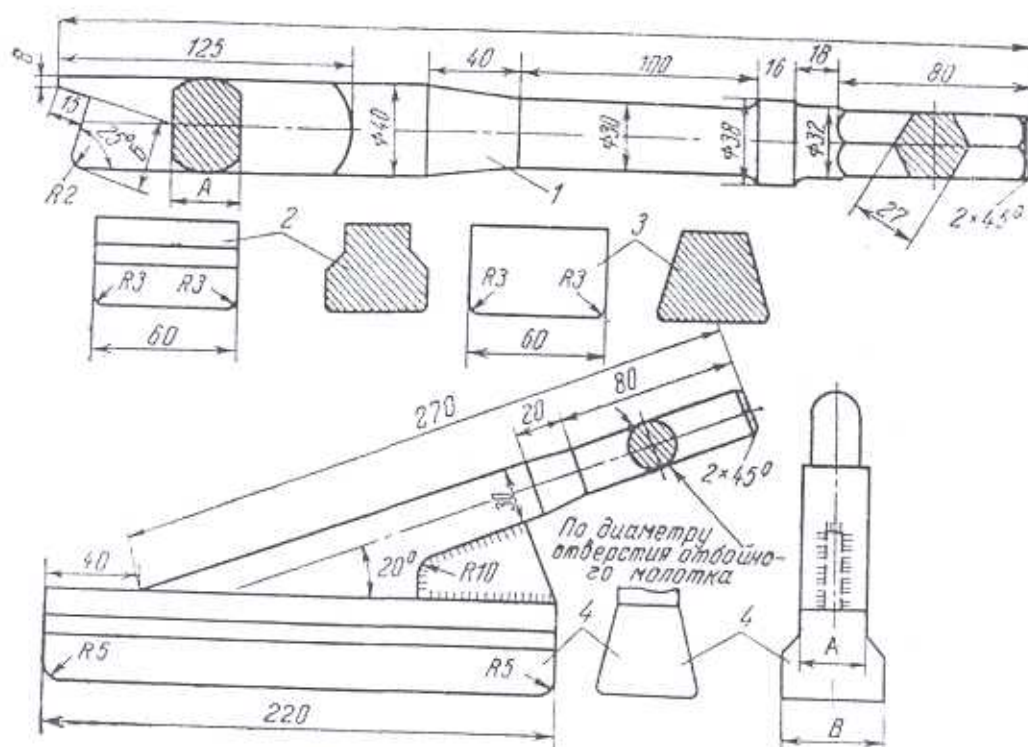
Выколотки для выбивки и забивки пазовых клиньев ротора:
